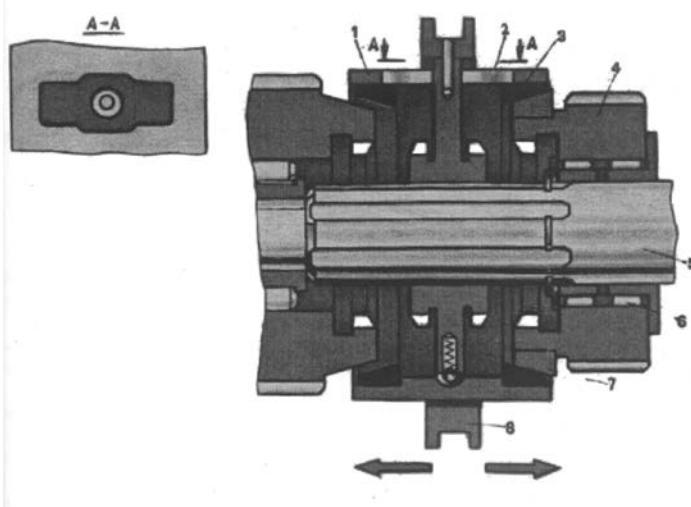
Синхронизатор коробки передач: 1-обойма; 2-прорезь; 3-корпус обоймы; 4-ведущая шестерня; 5-вал; 6-подшипник; 7-конус шестерни; 8-каретка.
